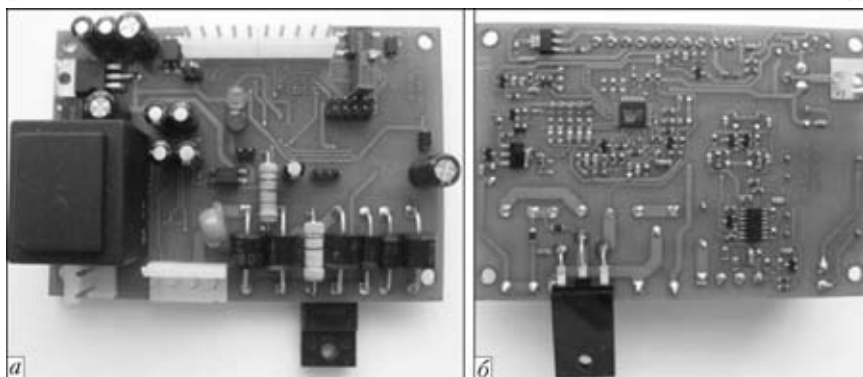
Внешний вид лицевой (а) и тыльной (б) сторон платы импульсного стабилизатора сварочной дуги переменного тока
